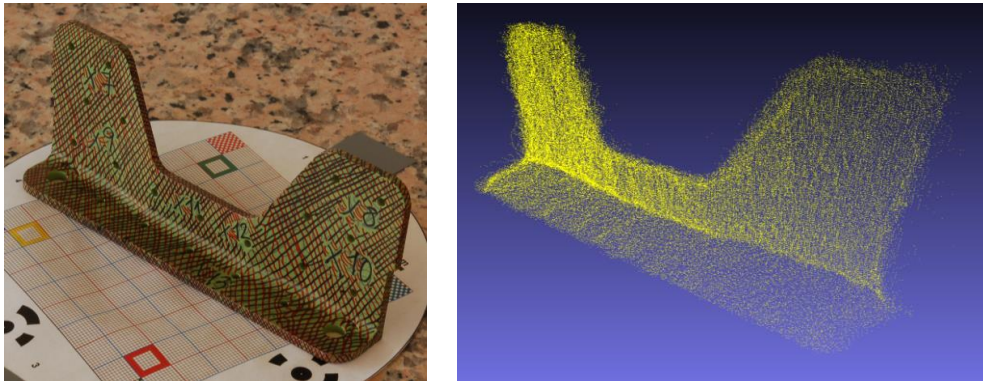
Pieza a escanear (izquierda) y nube de puntos (derecha)
